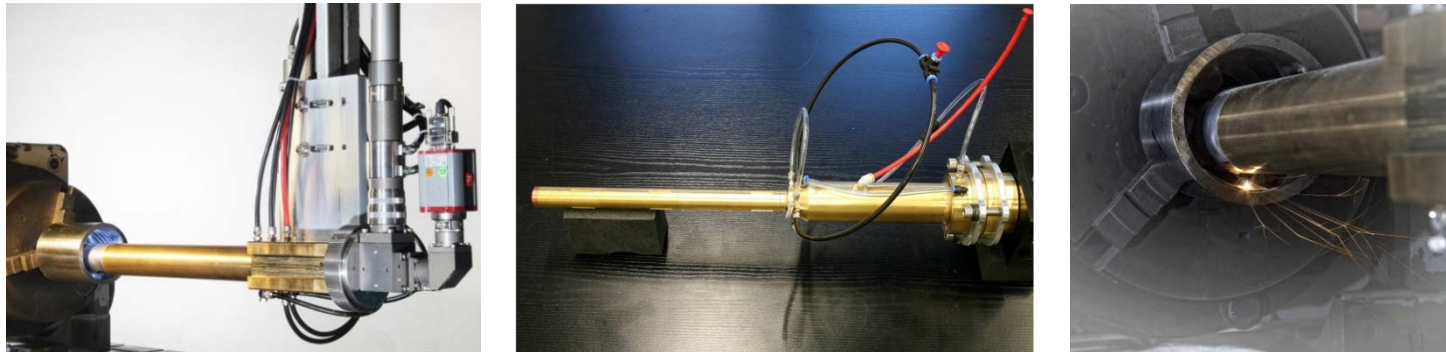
Mit 500 Millimetern Eintauchtiefe erlaubt die iClad® auch ab 30 Millimetern Innendurchmesser auftragsgeschweißte Korrosionsschutzschichten.
